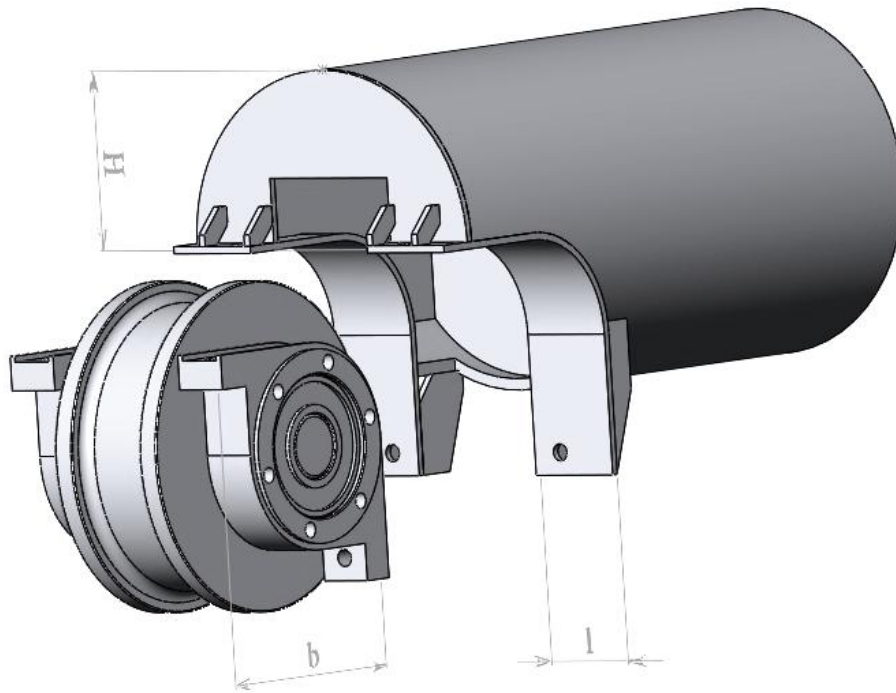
Предлагаемое соединение трубчатой ездовой балки с угловой буксой
